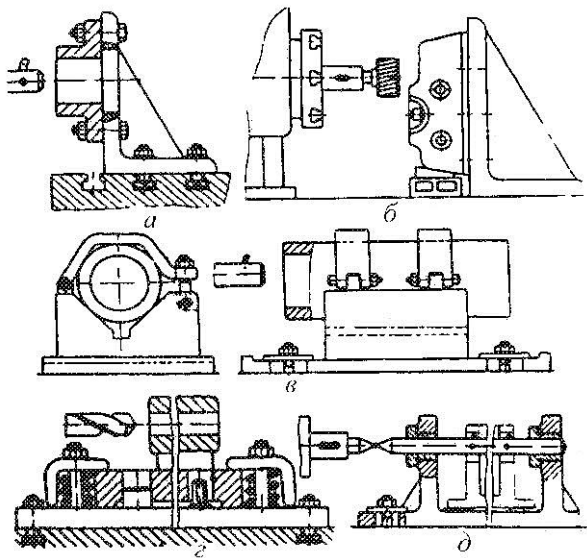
Установка і закріплення заготовок на розточувальних верстатах
